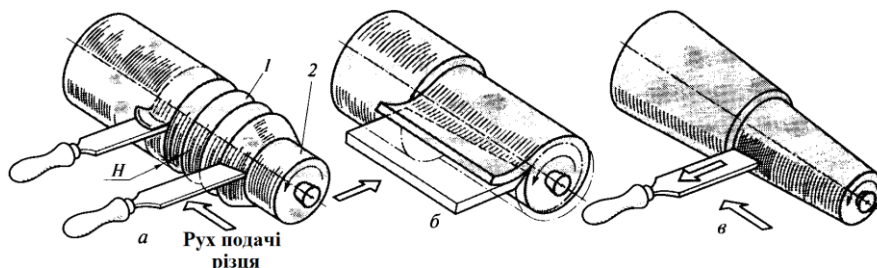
Схема точіння деталей різцем при подачі: а – поздовжній; б – поперечний; в – поздовжньо-поперечний; 1 – чорнова поверхня; 2 – чистова поверхня
